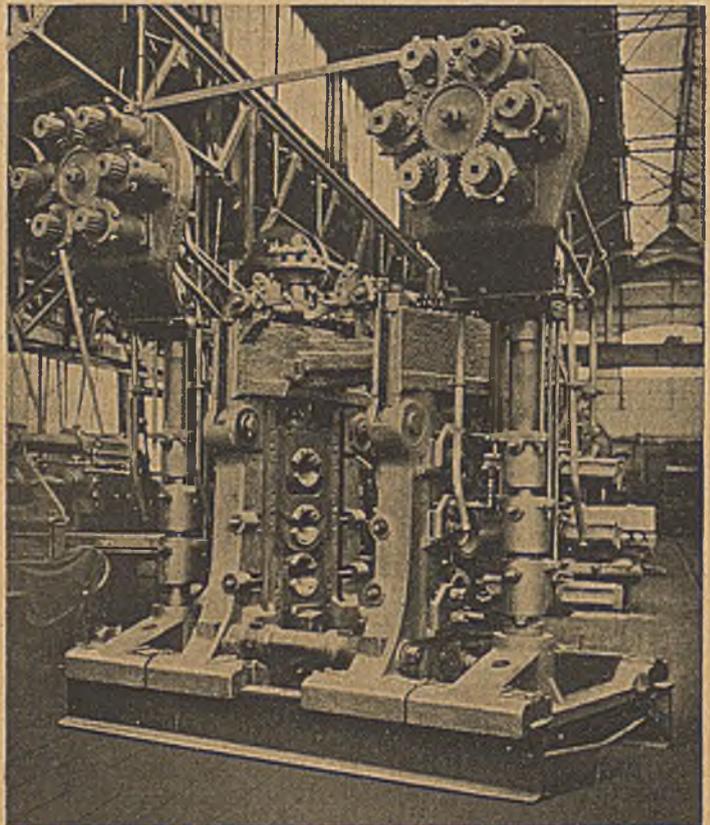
Feinstrabengerüst mit Schmiervorrichtung auf besonderem Ständer für Lagerung der Kuppelzapfeln.
